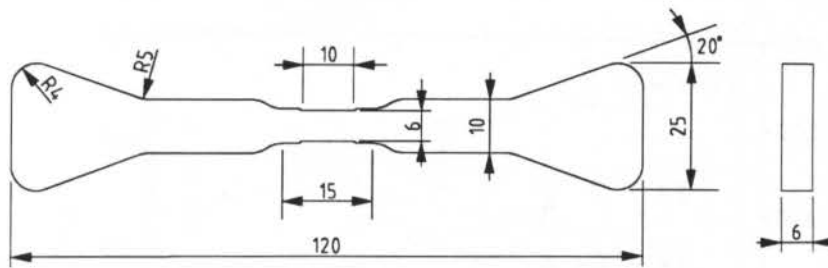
Geometria dos corpos de prova. Dimensões em mm
